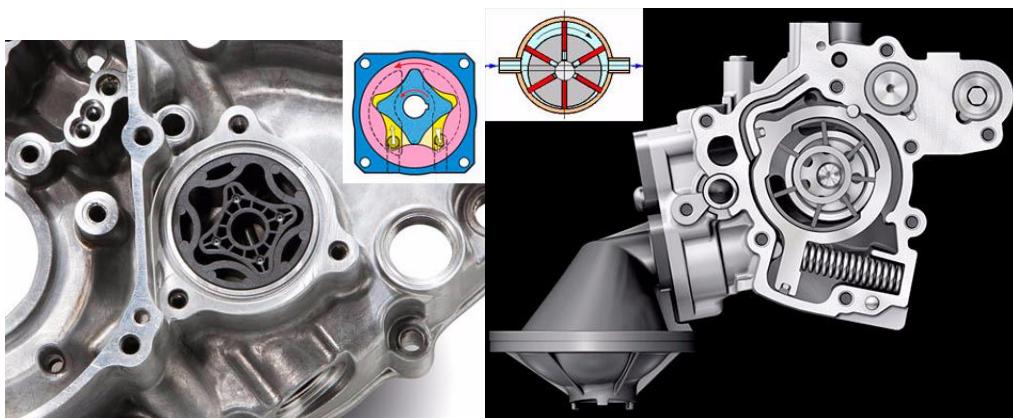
Роторний (а) та шиберний (б) оливний насос.
